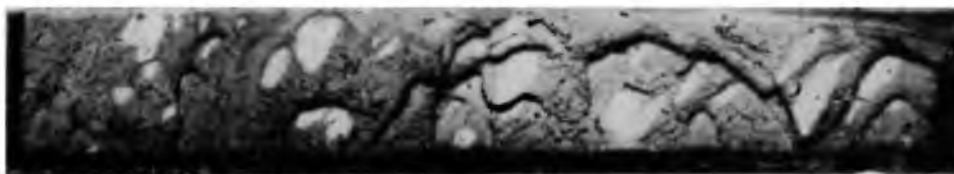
Характерный вид излома штамповки из алюминиевого сплава с макронесплошностями блестящего цвета
